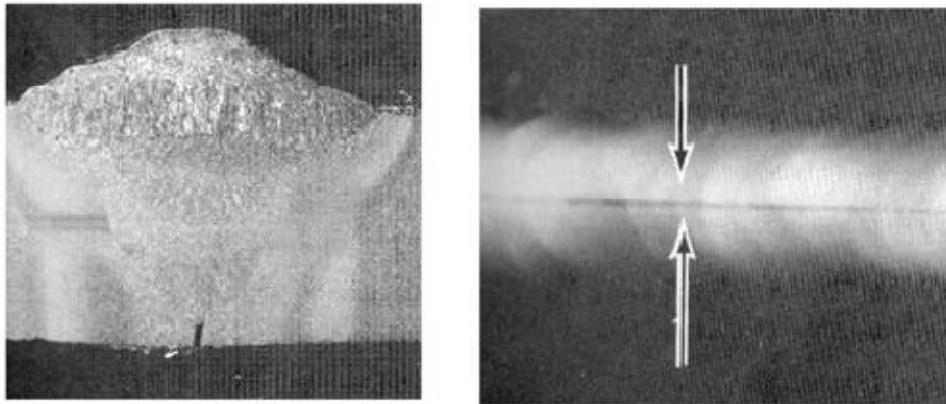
Foto (esquerda) e imagem radiográfica (direita) de uma junta soldada com falta de penetração
